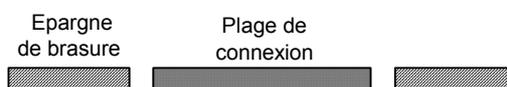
Forme d’une plage de connexion normale de la carte d’essai du montage de fiabilité
